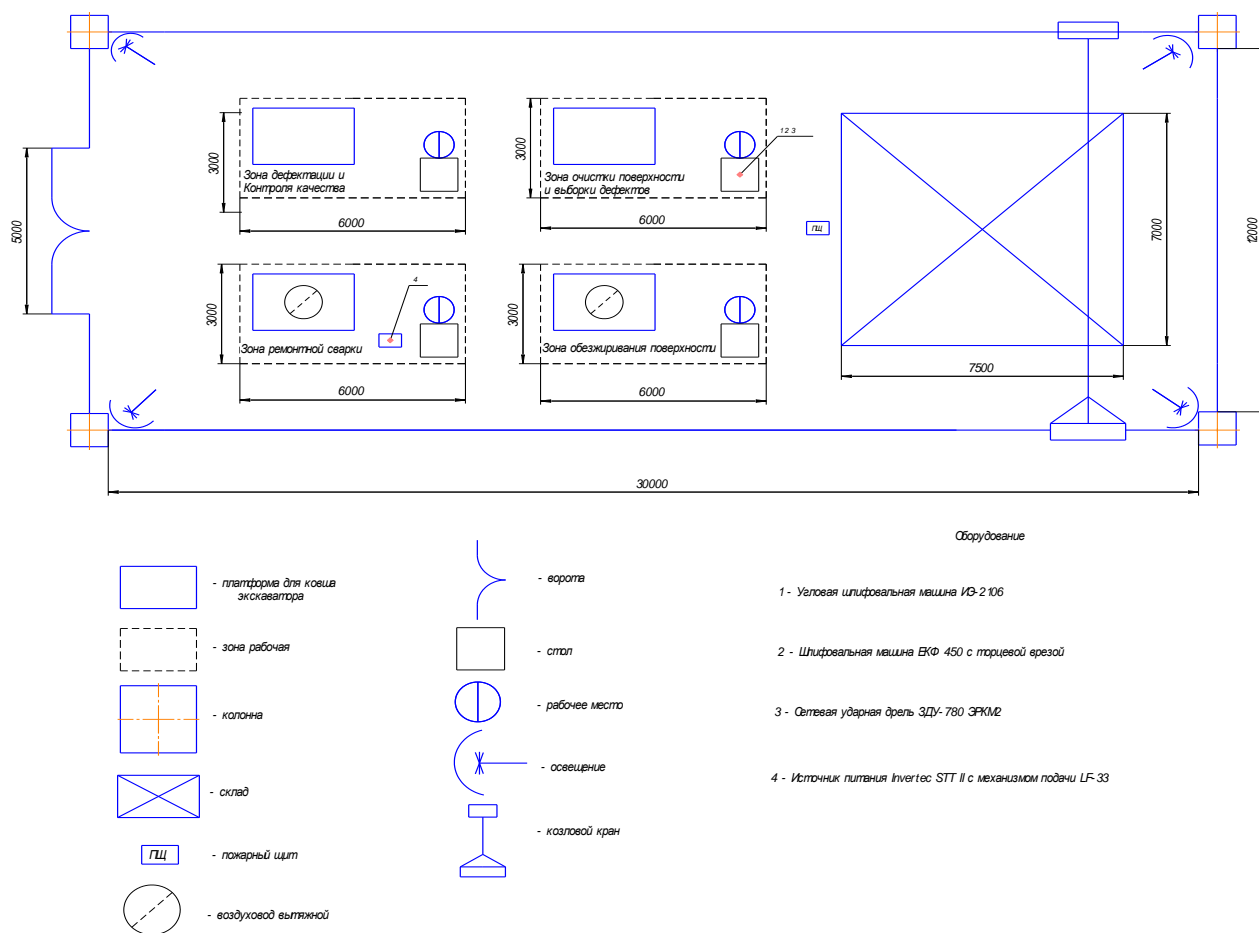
Планировка участка ремонта ковша экскаватора
